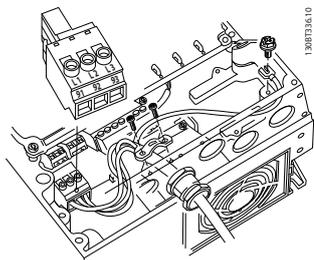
Connexion au secteur et à la terre sans sectionneur
